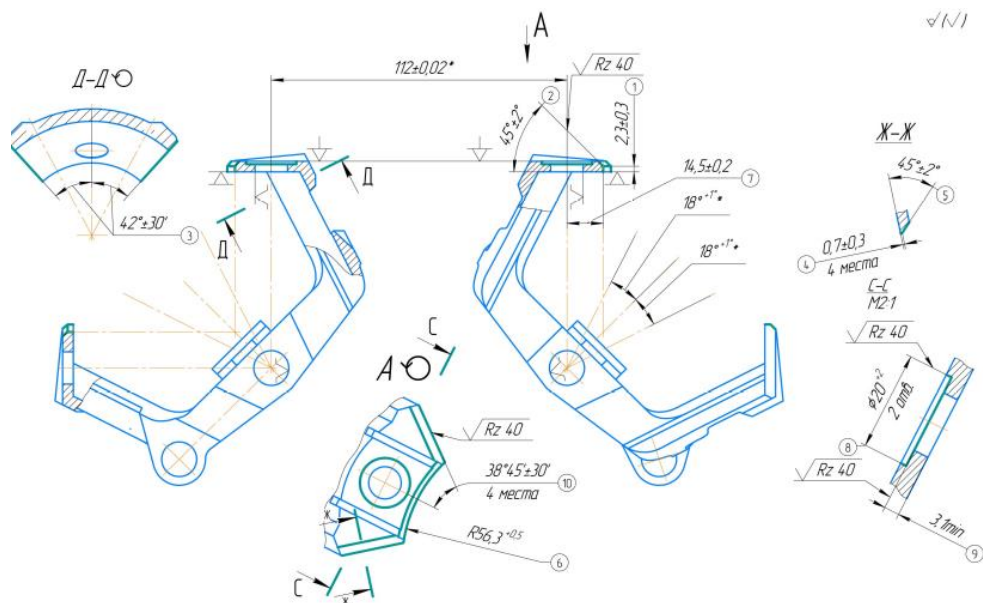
Эскиз к операции 110 – Фрезерная с ЧПУ
